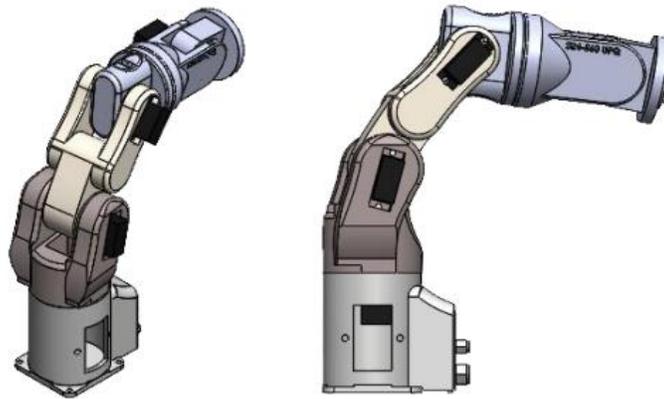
Vista isométrica (izquierda) y frontal (derecha) del desarrollo preliminar.
